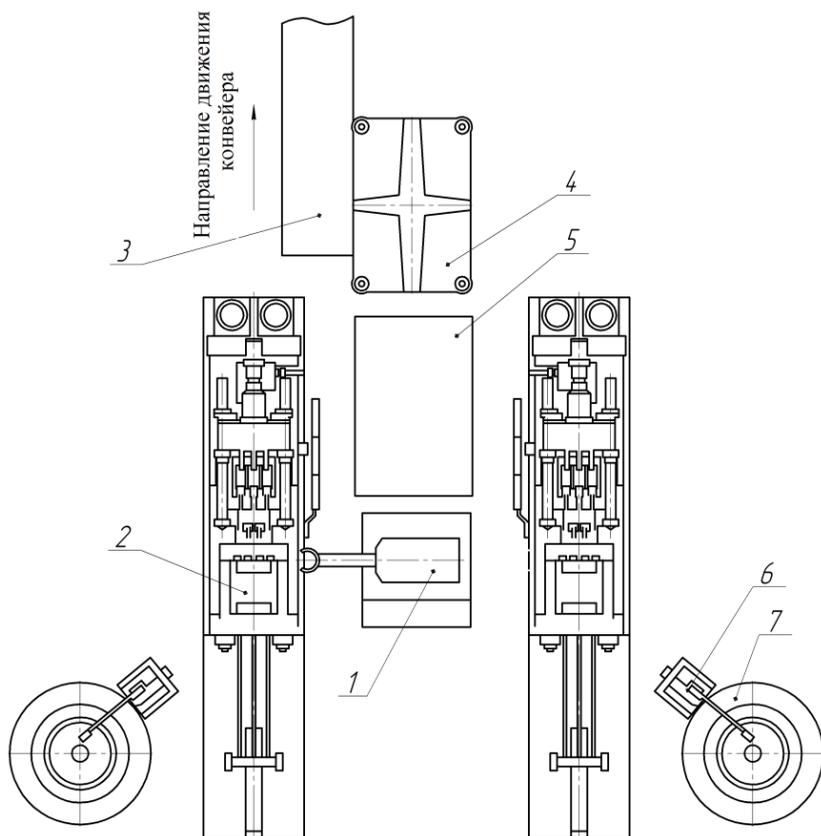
Роботизированный комплекс литья под давлением: 1 – робот; 2 – машины литья под давлением; 3 – отводящий конвейер; 4 – обрубной пресс; 5 – ванна с охлаждающей жидкостью; 6 – автооператор-заливщик; 7 – раздаточная электропечь
